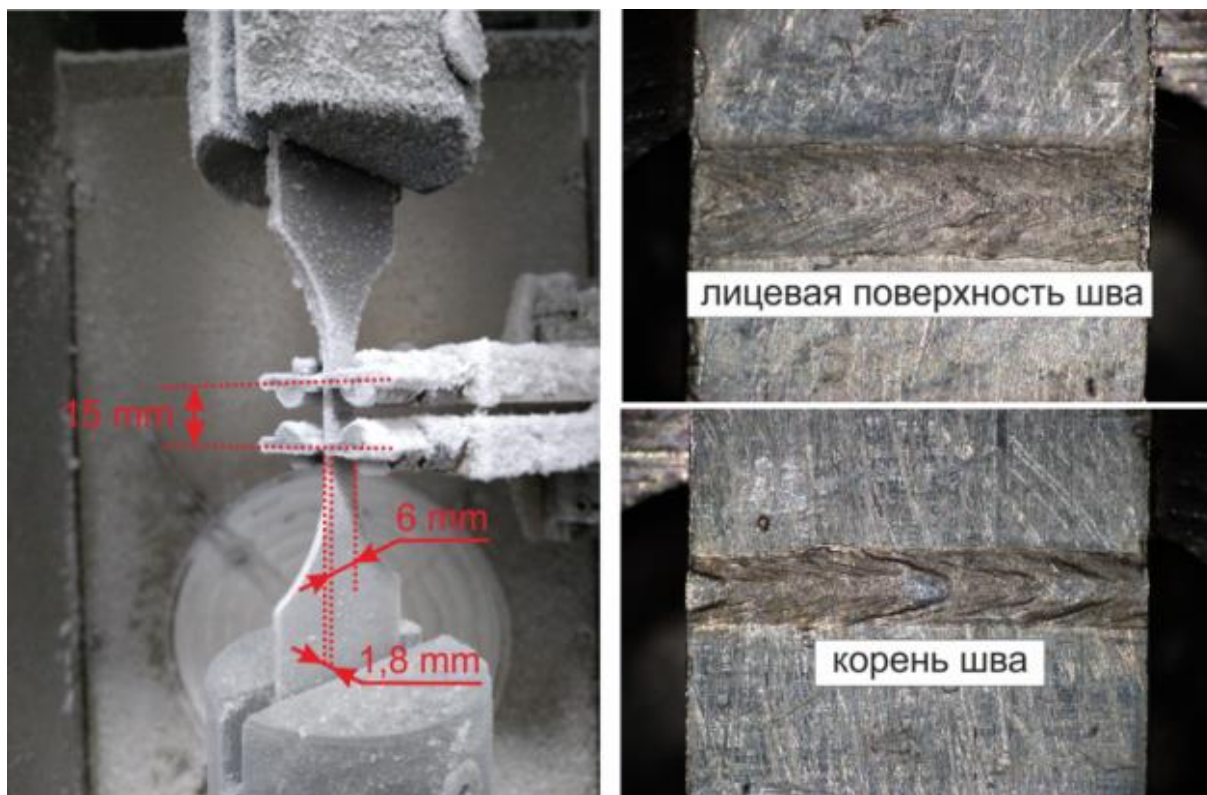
Образец со сварным соединением сплава В-1461 при испытании в термокамере с установленными щупами экстензометра (сварной шов находится между верхними и нижними щупами).
